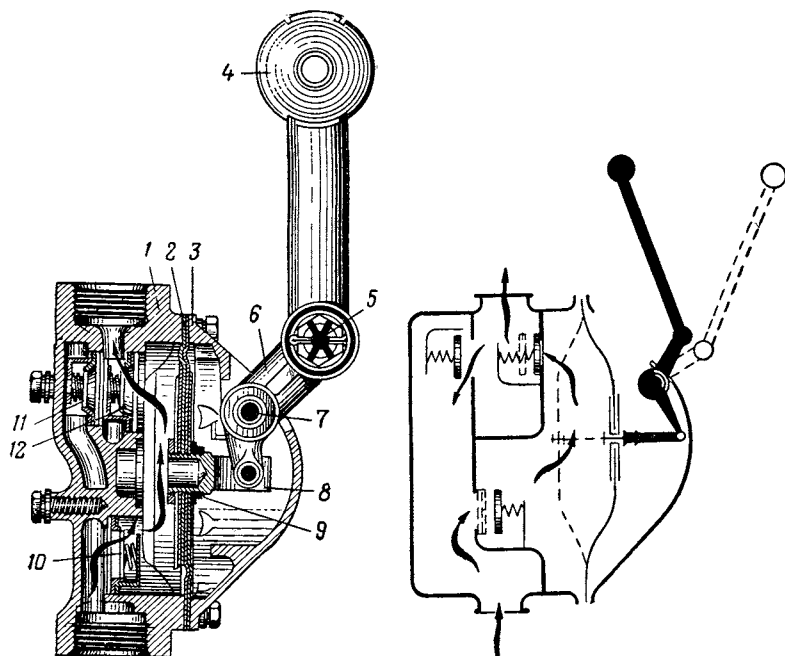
Ручной топливоподкачивающий насос РНМ-1:
